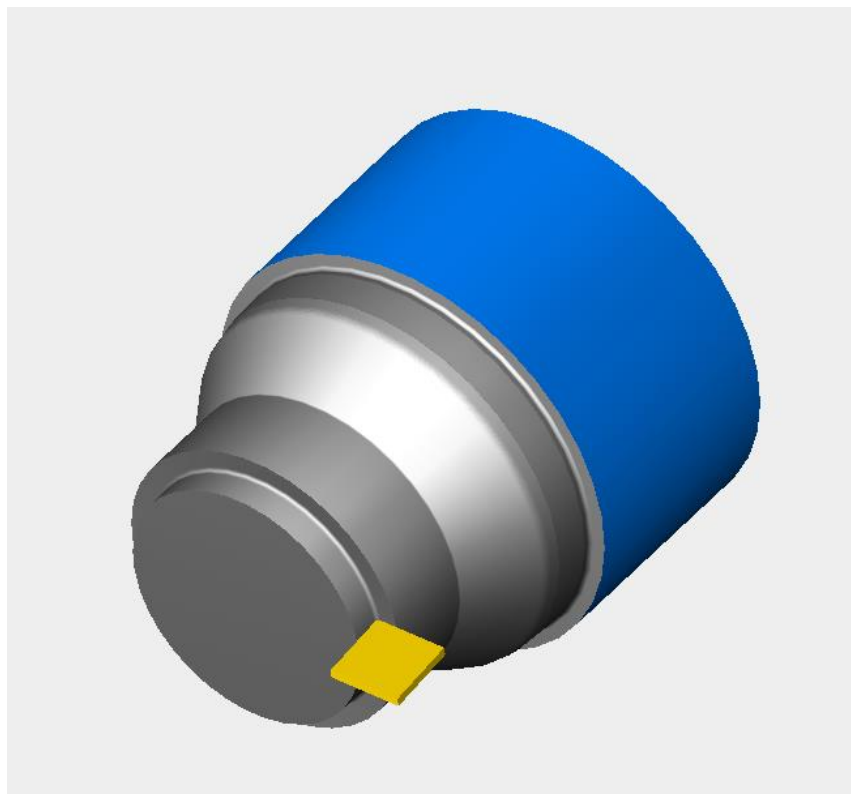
Токарна обробка зовнішньої циліндричної поверхні деталі «Корпус фрези торцевої»
